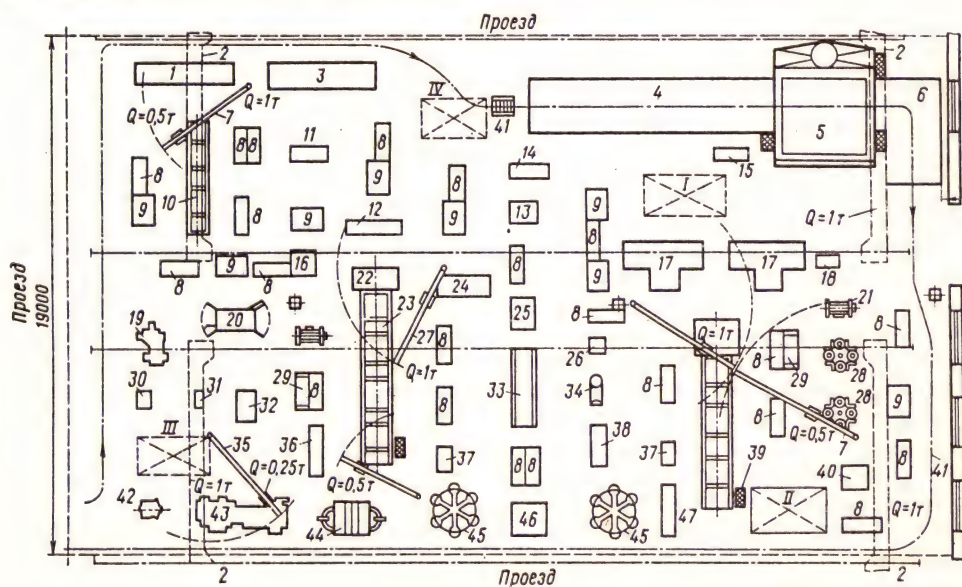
Планировка участка ремонта и сборки агрегатов агрегаторемонтного завода с годовой программой 15 000 КР комплектов агрегатов автомобиля ЗИЛ-130
